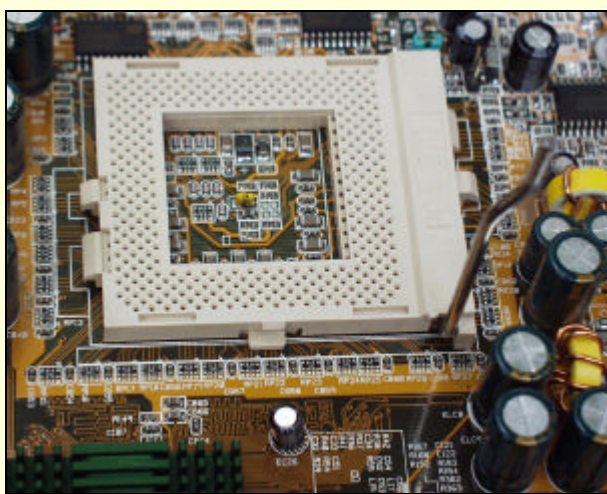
找到 Socket 370 插槽的第一支脚的位置
